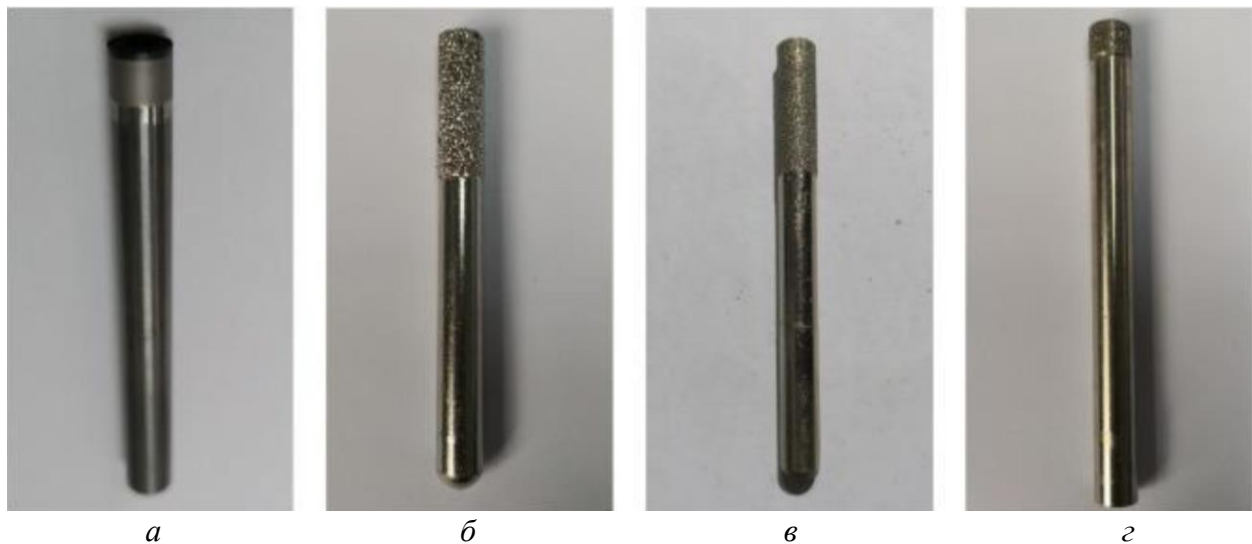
Фрезерно-шліфувальний інструмент, використаний в роботі [9]: а – PDC; б – 50#BDT; в – 200#BDT; г – 100#EDT
